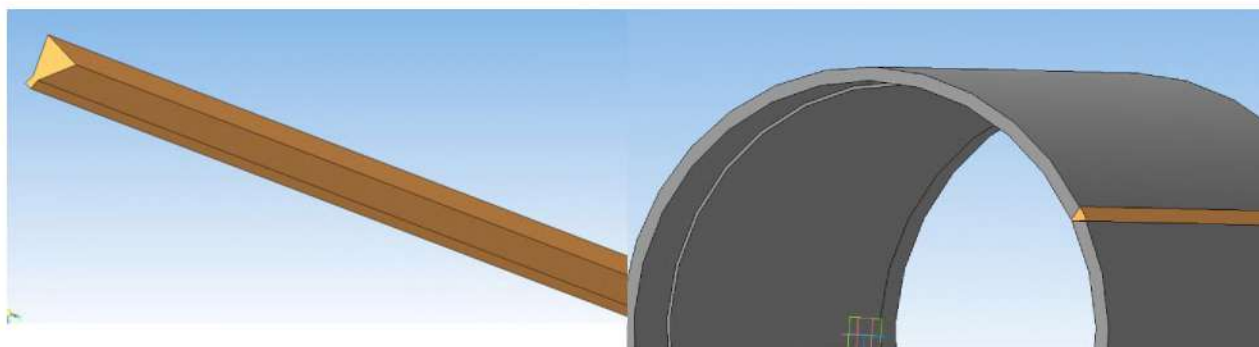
Создание и установка сварочного шва в обечайку
